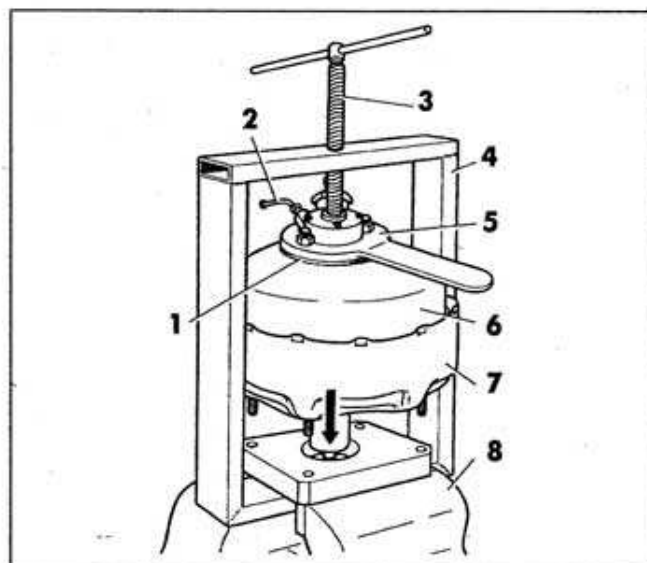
Приспособление 6999–7567 для разборки и сборки усилителя: 1 – прокладка; 2 – трубка; 3 – винт; 4 – приспособление; 5 – заглушка; 6 – крышка; 7 – корпус; 8 – тиски
